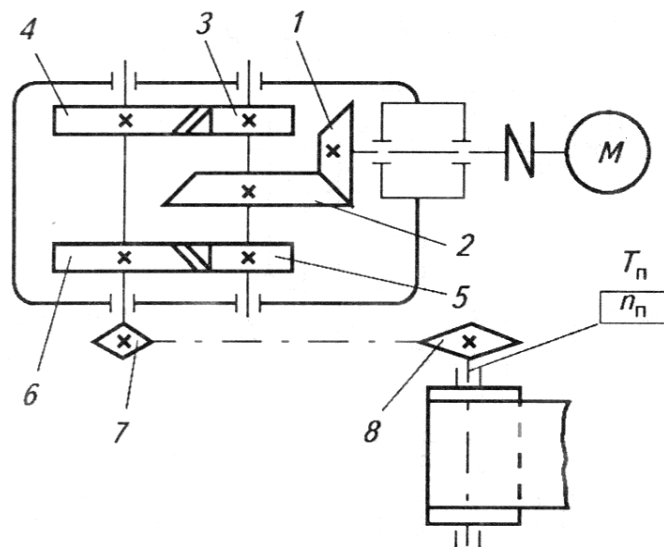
Кинематическая схема привода, состоящего из электродвигателя, коническо-цилиндрического редуктора и цепной передачи: 1 – коническая шестерня; 2 – коническое колесо; 3, 5 – цилиндрические шестерни; 4, 6 – цилиндрические колеса; 7, 8 – звездочки цепной передачи;  $M$  – электродвигатель
